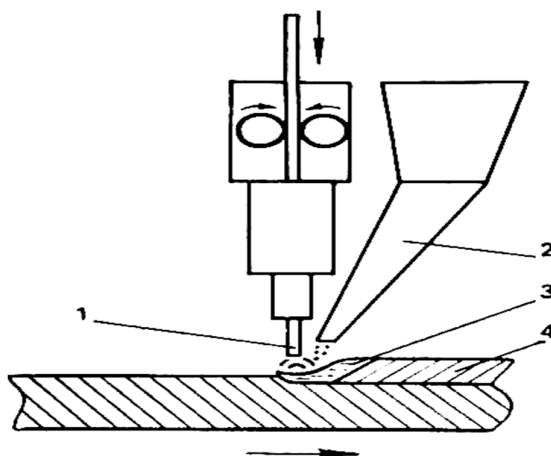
Наплавка с подачей порошка в сварочную ванну: 1 – электрод; 2 – бункер с порошком; 3 – сварочная ванна; 4 – покрытие.
